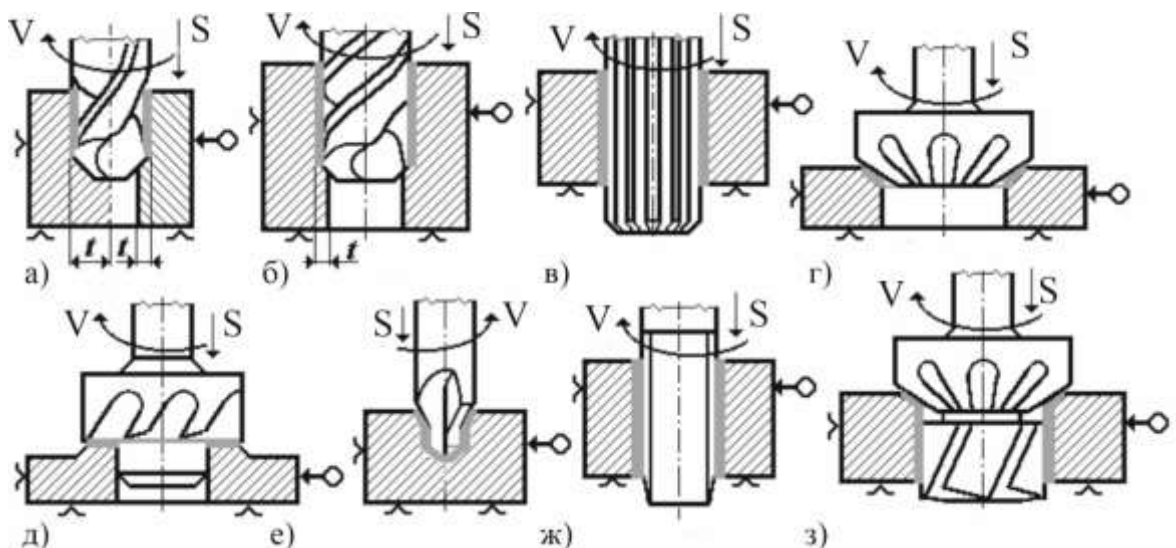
Схеми обробки внутрішніх циліндричних поверхонь кінцевим інструментом: t - величина припуску; а – розсвердлювання; б – зенкерування; в – розгортання; г - зенкування; д - цекування; е – зацентрування (свердління центрувальним свердлом); ж – нарізування різьблення; з – комбінована обробка кількох поверхонь.
